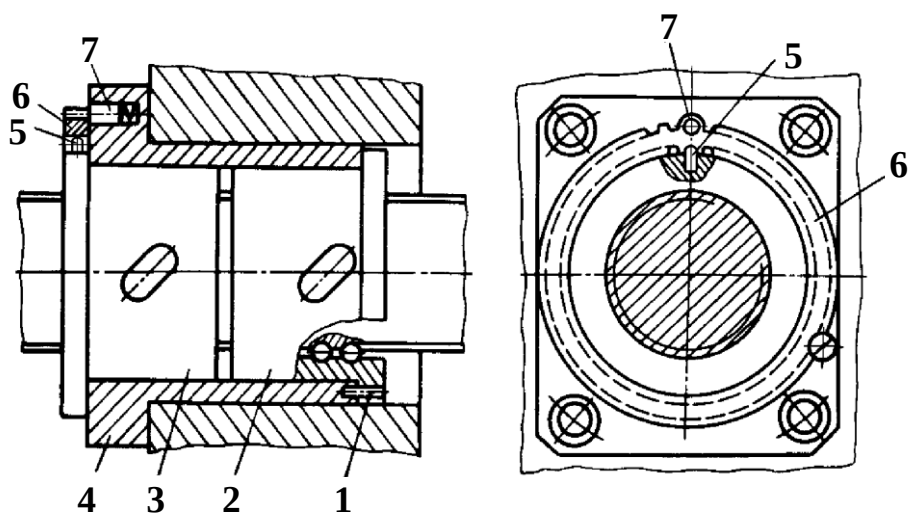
Конструкція передачі з одностороннім регулюванням натягу
